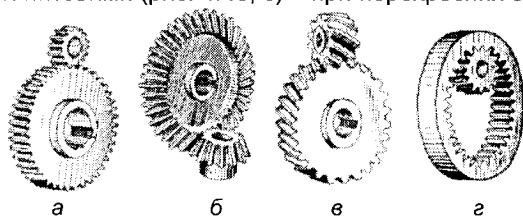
Види зубчастих передач: а – циліндрична зовнішнього зачеплення; б – конічна; в – гвинтова; г – циліндрична внутрішнього зачеплення
